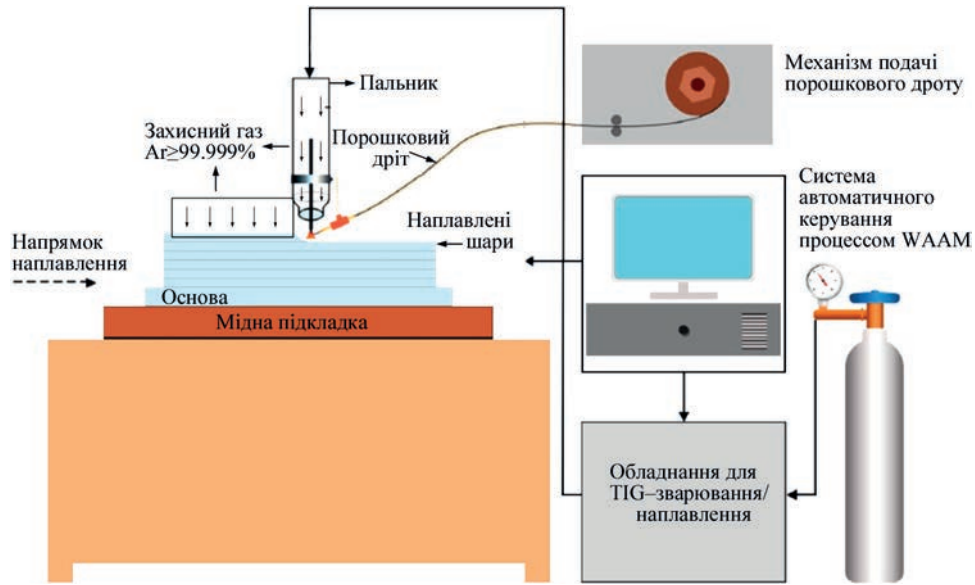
Схема установки для пошарового наплавлення TIG способом із присадним металопорошковим дротом
